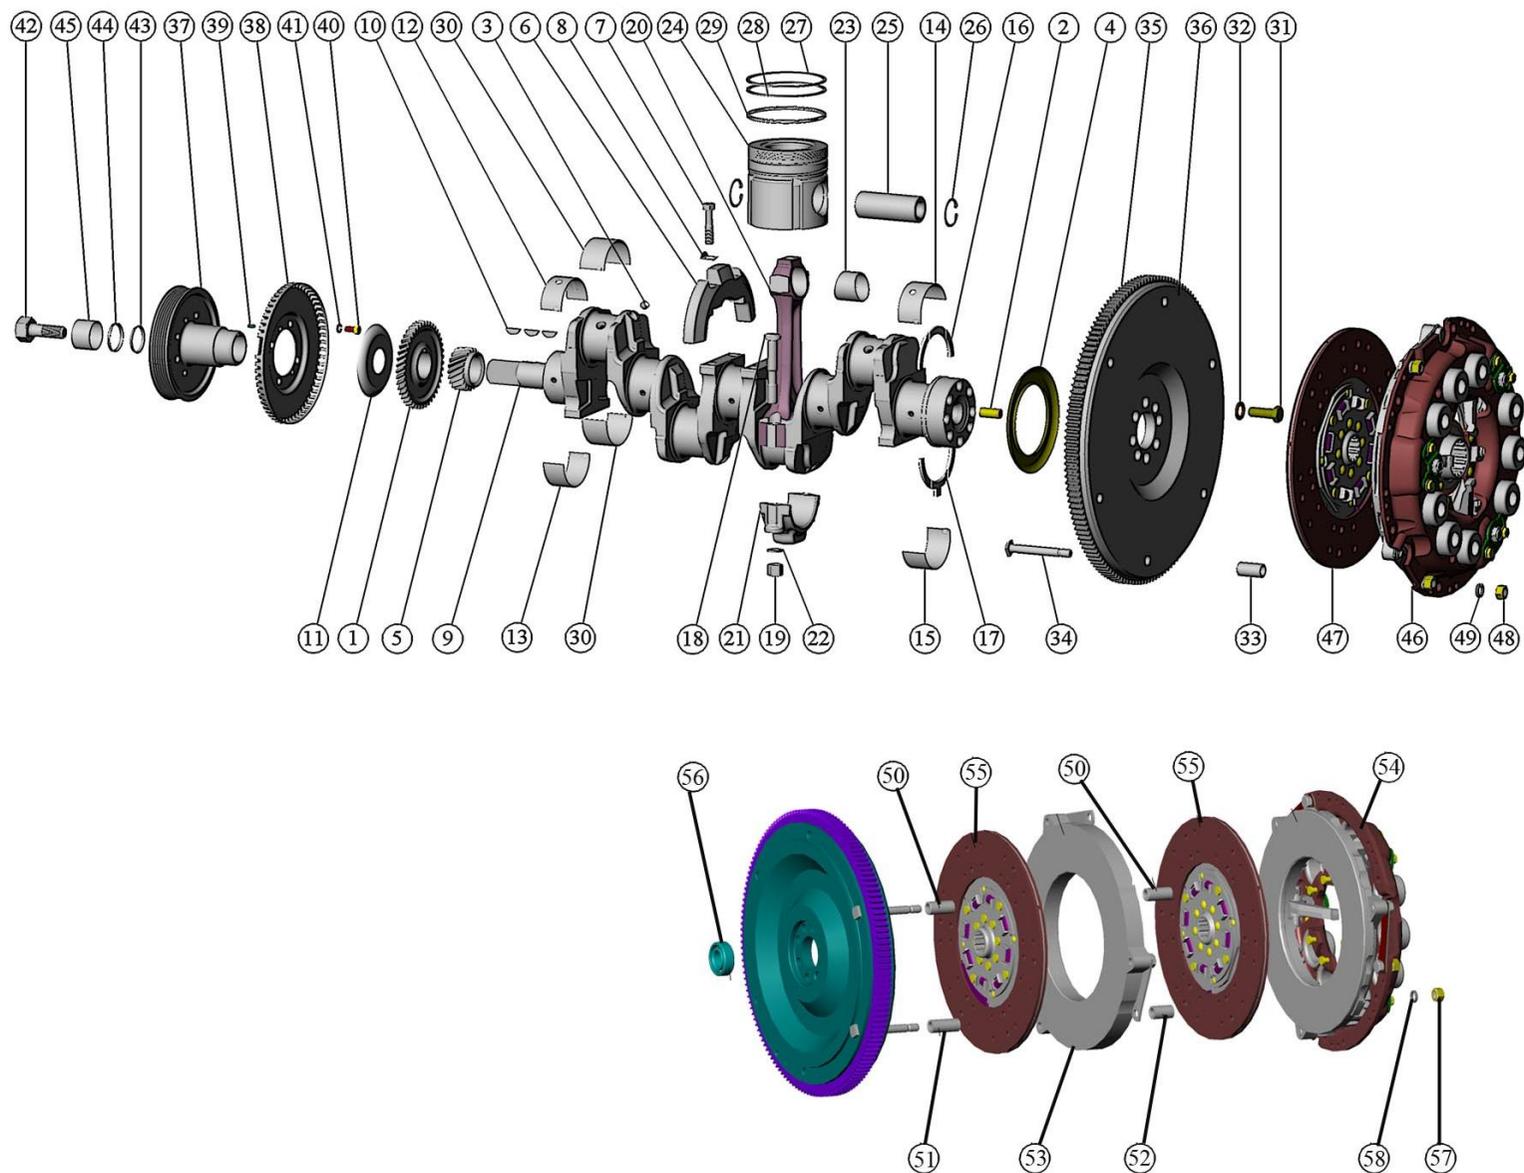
Кривошипно-шатунный механизм. Установка муфты сцепления.
